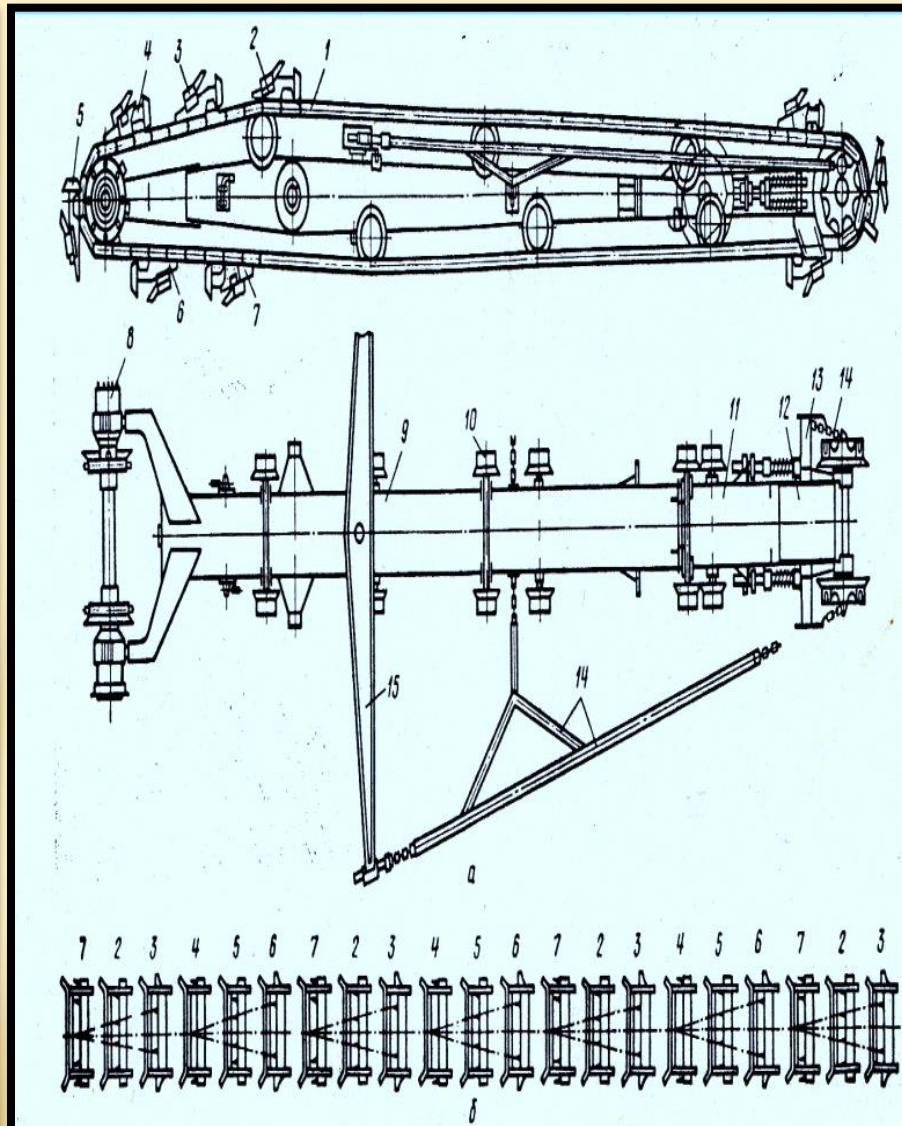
Рабочий орган экскаватора ЭТЦ-252:
